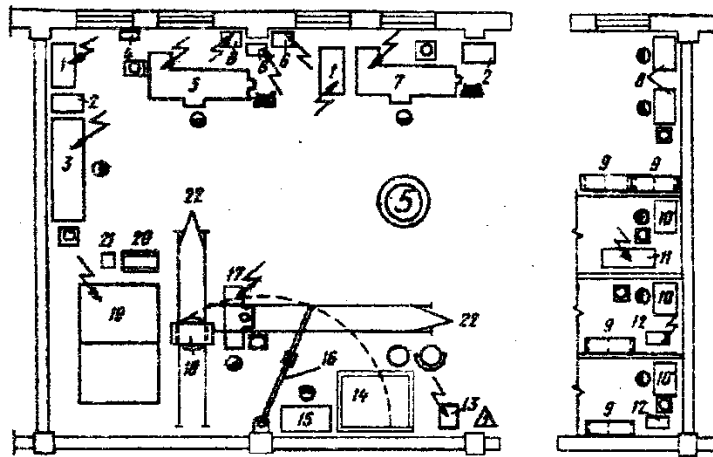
Схема приблизного планування зварювально-наплавлювального відділення: 1 - зварювальний перетворювач; 2 - розподільний пристрій; 3 - зварювальний TIG пристрій; 4 - регулятор зварювального трансформатора; 5 - верстат для вібродугового наплавлення; 6 - електровипрямлячі; 7 - верстат для наплавлення під шаром флюсу або у захисних газах; 8 - столи для газозварювальних робіт; 9 - стелажі для деталей; 10 - столи для електродугового зварювання; 11 - зварювальний перетворювач; 12 - зварювальний трансформатор; 13 - верстат з гнучким валом для шліфування; 14 - копильник для охолодження деталей; 15 - слюсарний верстат; 16 - консольний поворотний кран; 17 - зварювальний стенд; 18 - візок; 19 - нагрівальна муфельна піч; 20 - стіл для піддонів; 21 - ящик для піску; 22 - рейковий шлях.
